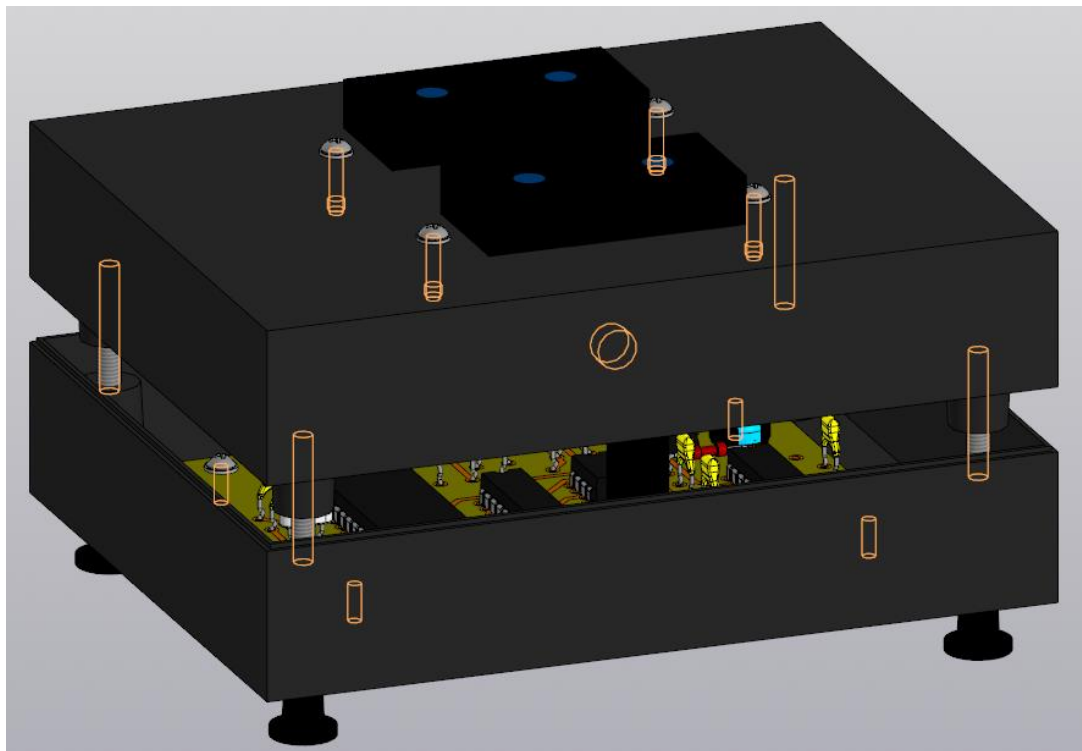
3D модель пристрою, загальний вигляд
